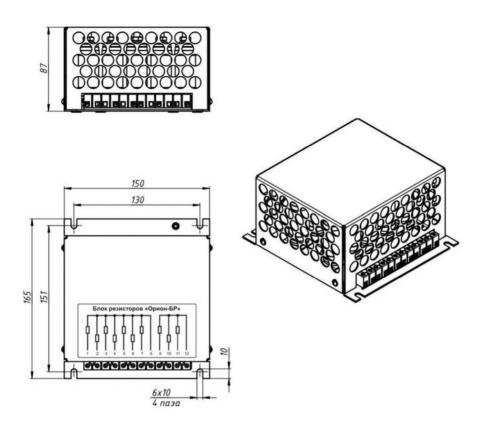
Внешний вид, габаритные и присоединительные размеры блока резисторов «Орион-БР»
